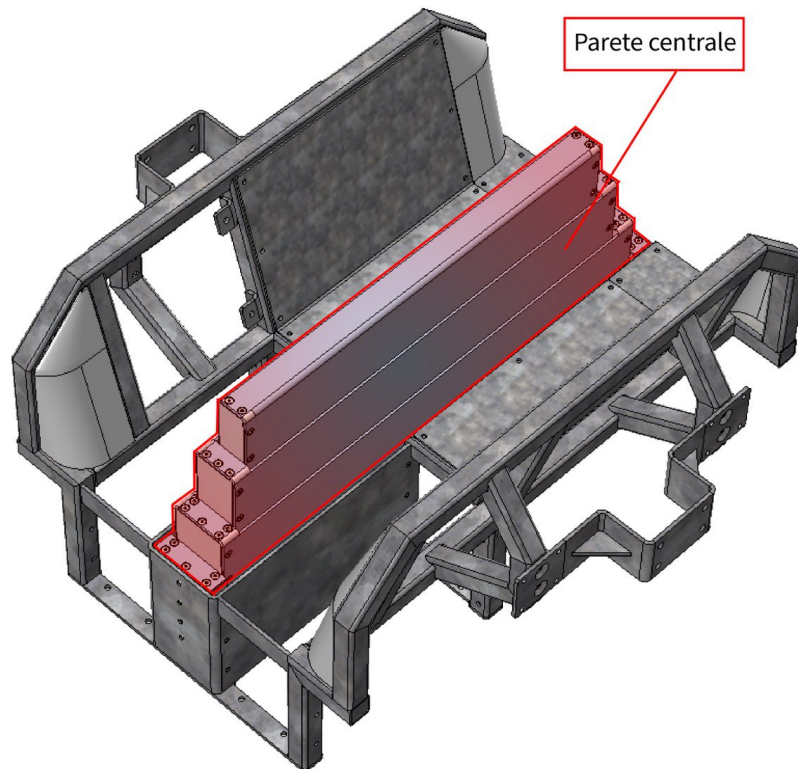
Dettaglio della parete centrale pieghevole alzata, inglobata nel supporto addominale
